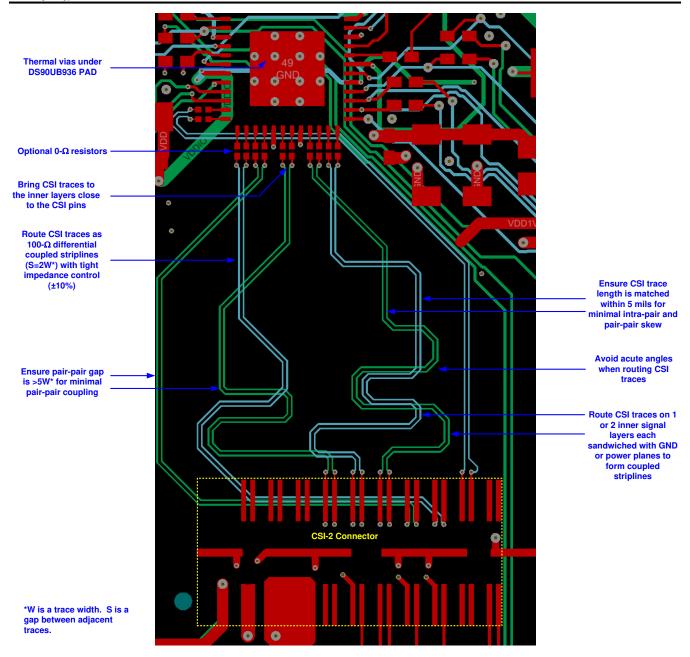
DS90UB936-Q1 PCB Layout Example: CSI-2 Traces
